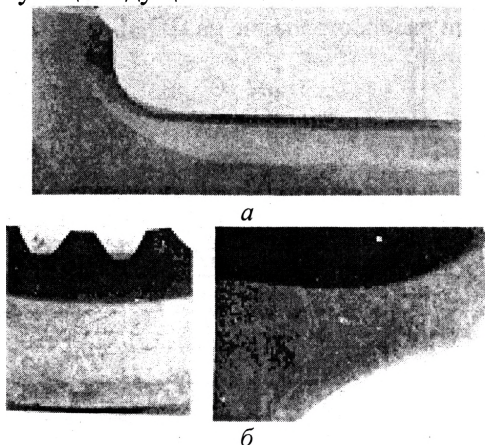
Зоны закалки в сечении деталей: а — поворотный кулак, б — ступица ведущего моста
